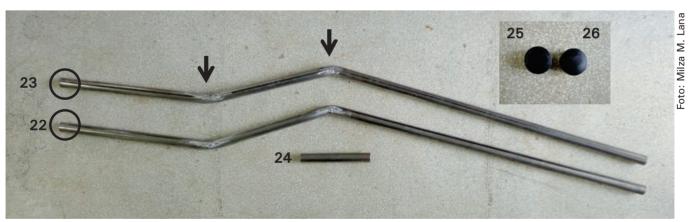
Partes componentes do chassi, Embrapa Hortaliças, 2014.
